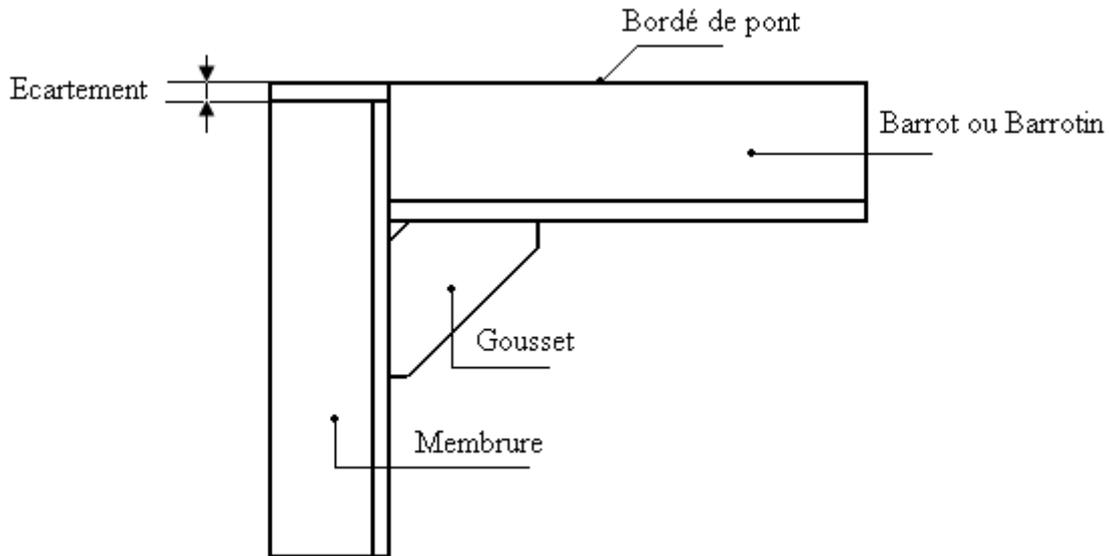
Jonction barrot du pont avec membrure de la muraille.
